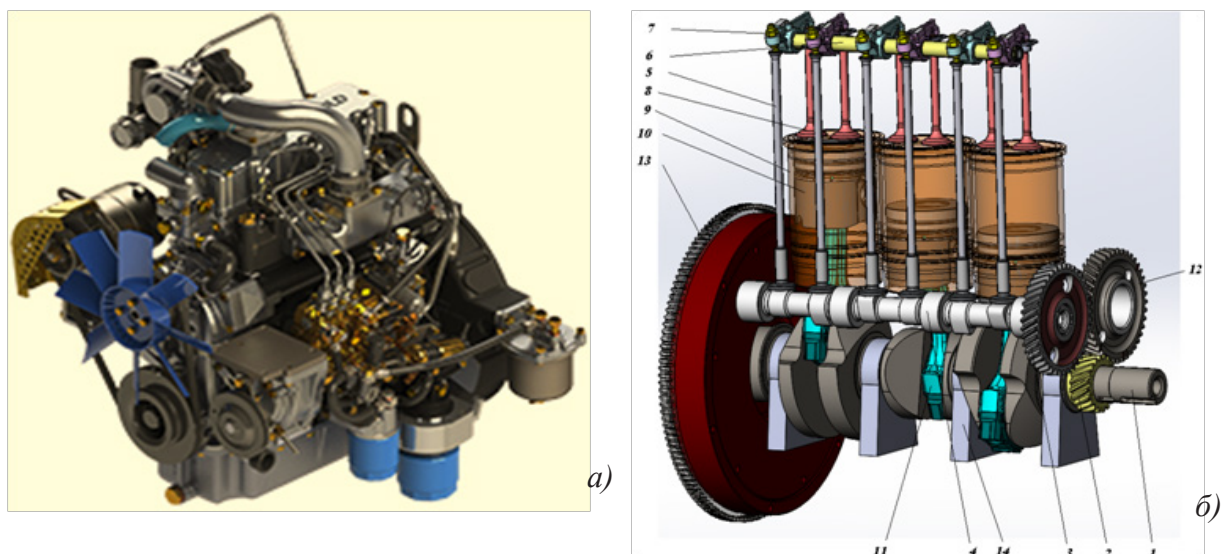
Внешний вид двигателя MMZ-3LDT (а) и модель (б) его ЦПГ и ГРМ
